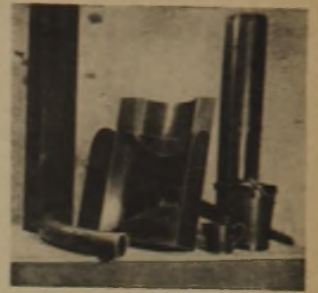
Geschweißte Formteile aus Mipolam — PCU. Hersteller: Schrupp & Müller, Betzdorf (Sieg)
